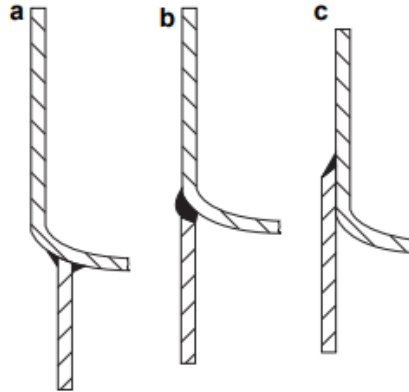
Soldaduras: a) de cabezal inferior b) a ras de la carcasa c) al exterior de la carcasa (5)
